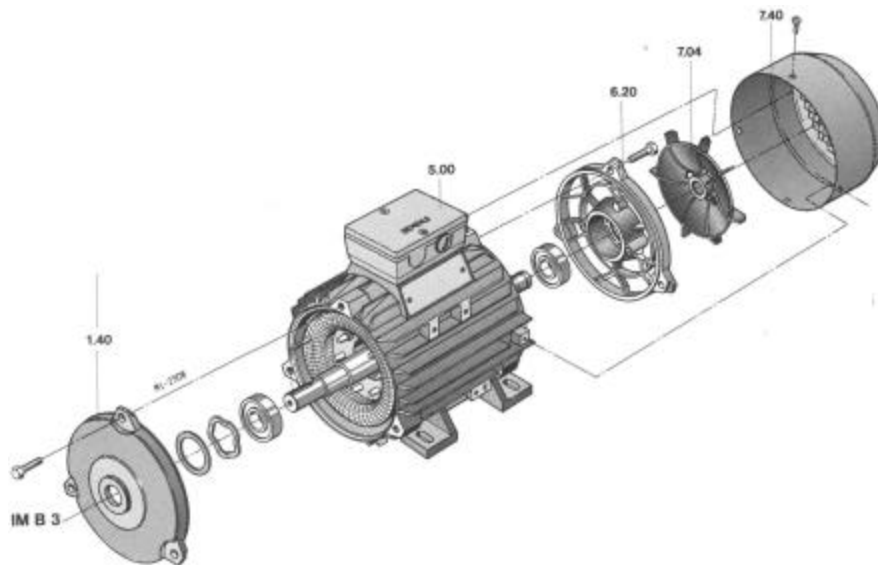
Partes componentes de un motor de inducción trifásico jaula de ardilla.
